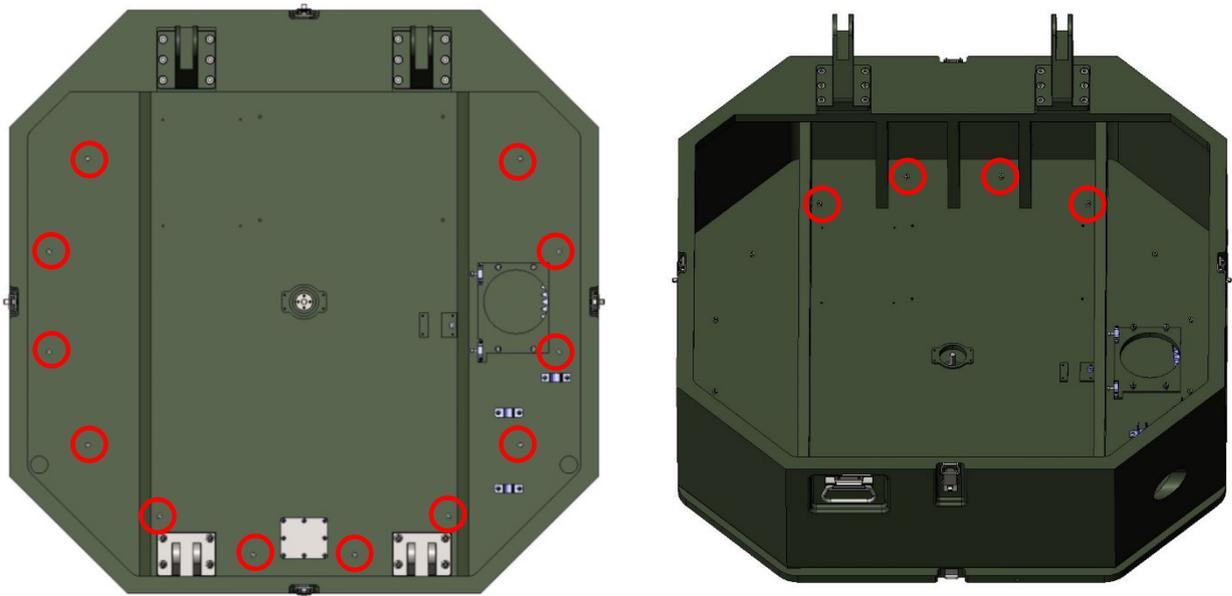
Демонтаж подвижной части корпуса ОПУ
